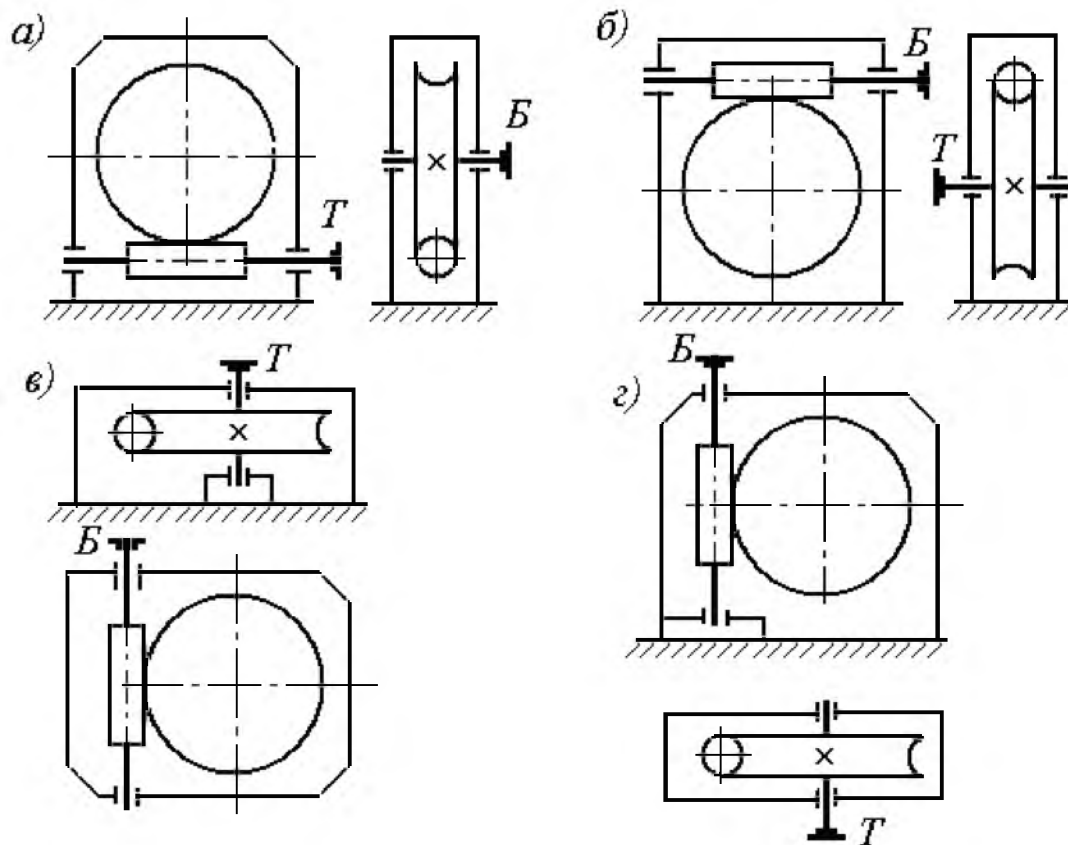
Кинематические схемы одноступенчатых червячных редукторов
